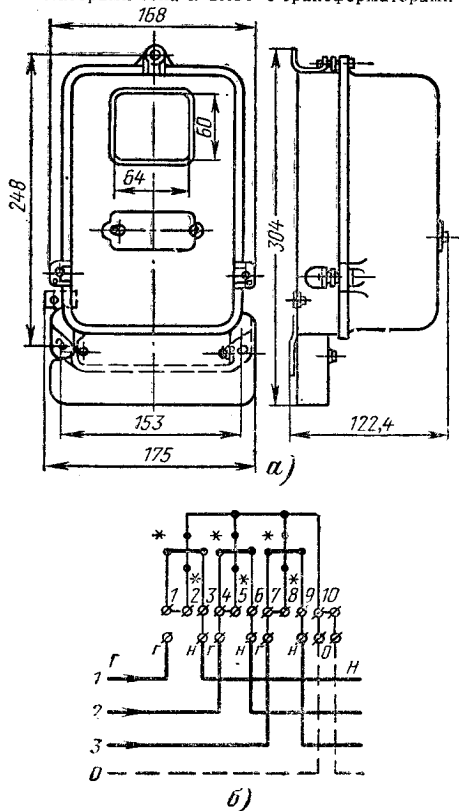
Габаритный чертеж и схема включения счетчиков типа СА4, СА4У.
